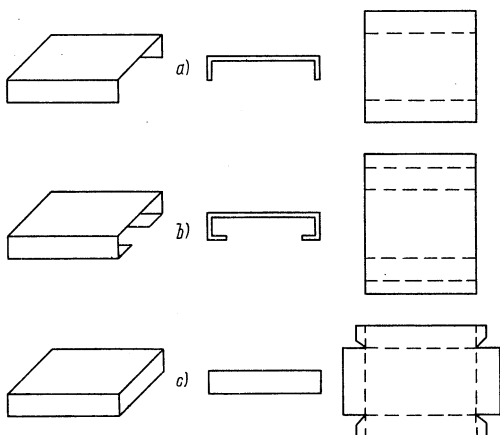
Chassisformen I; a — einfaches U-förmiges Chassis, b — doppelt gebogenes U-förmiges Chassis, c — allseitig abgebogenes kastenförmiges Chassis
